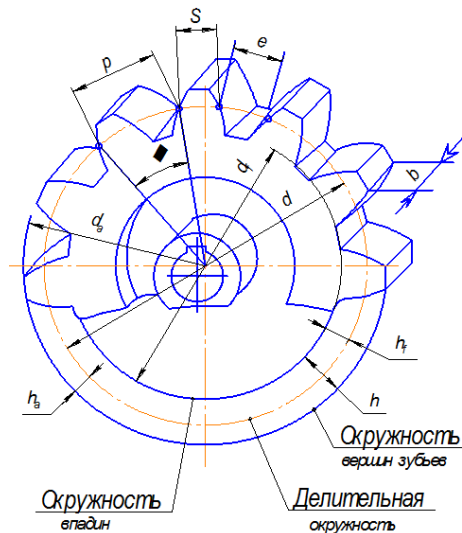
Геометрические параметры цилиндрического колеса с прямыми зубьями
